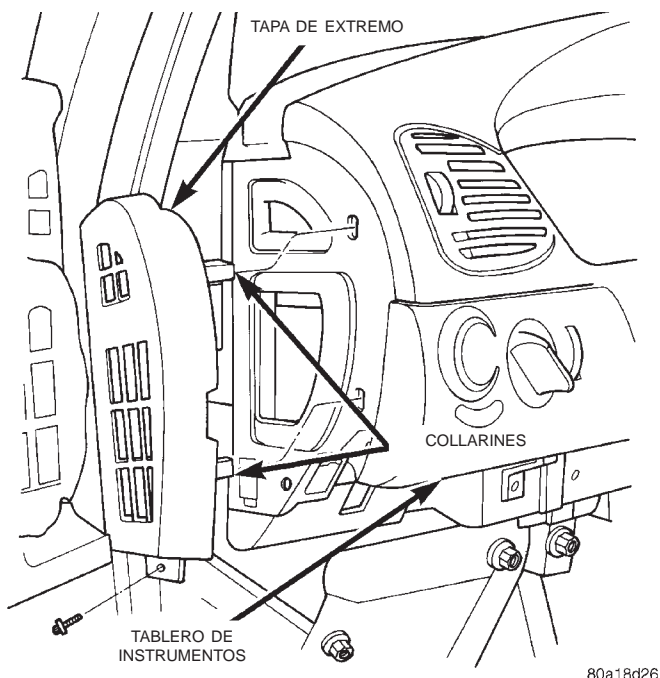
Tapa de extremo izquierdo del tablero de instrumentos
